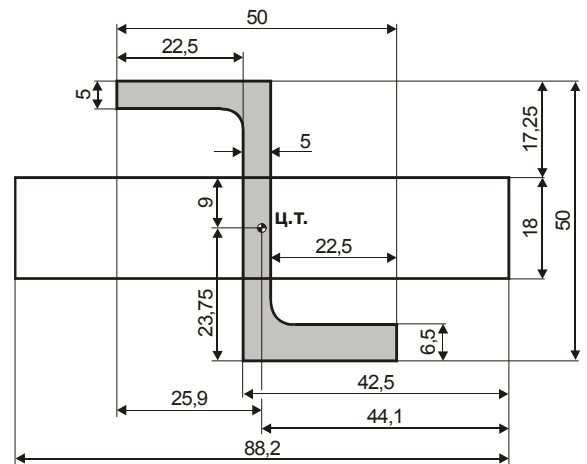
Центры тяжести регулярной зоны и захватов образцов
